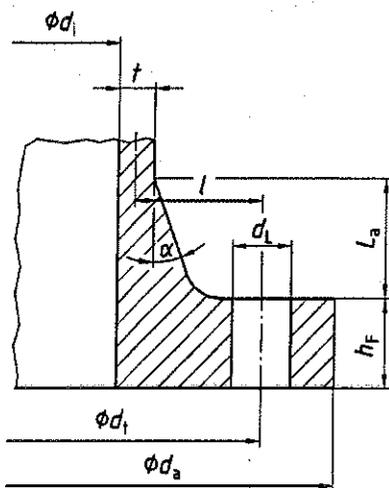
Vorschweißflansch (ohne Dichtung dargestellt)
